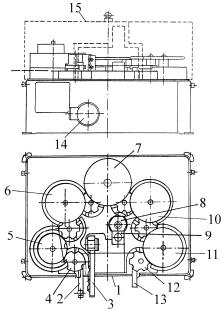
Многоцелевая автоматическая машина КАН-О-МАТ: 1 – станина машины; 2 – транспортер подачи корпусов; 3 – шнековый разделитель; 4 – звезда загрузочная; 5 – механизм сепарирования корпусов; 6 – механизм осадки корпусов; 7 – механизм отбортовки корпусов; 8 – механизм отделения крышки; 9 – магазин крышек; 10 – механизм закаточный первой операции; 11 – механизм закаточный второй операции; 12 – звезда разгрузочная; 13 – течка разгрузочная; 14 – электродвигатель; 15 – шумозащитный корпус
